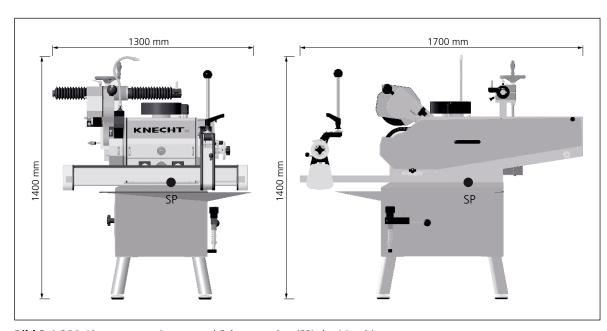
S20 Abmessungen in mm und Schwerpunkte (SP) der Maschine
